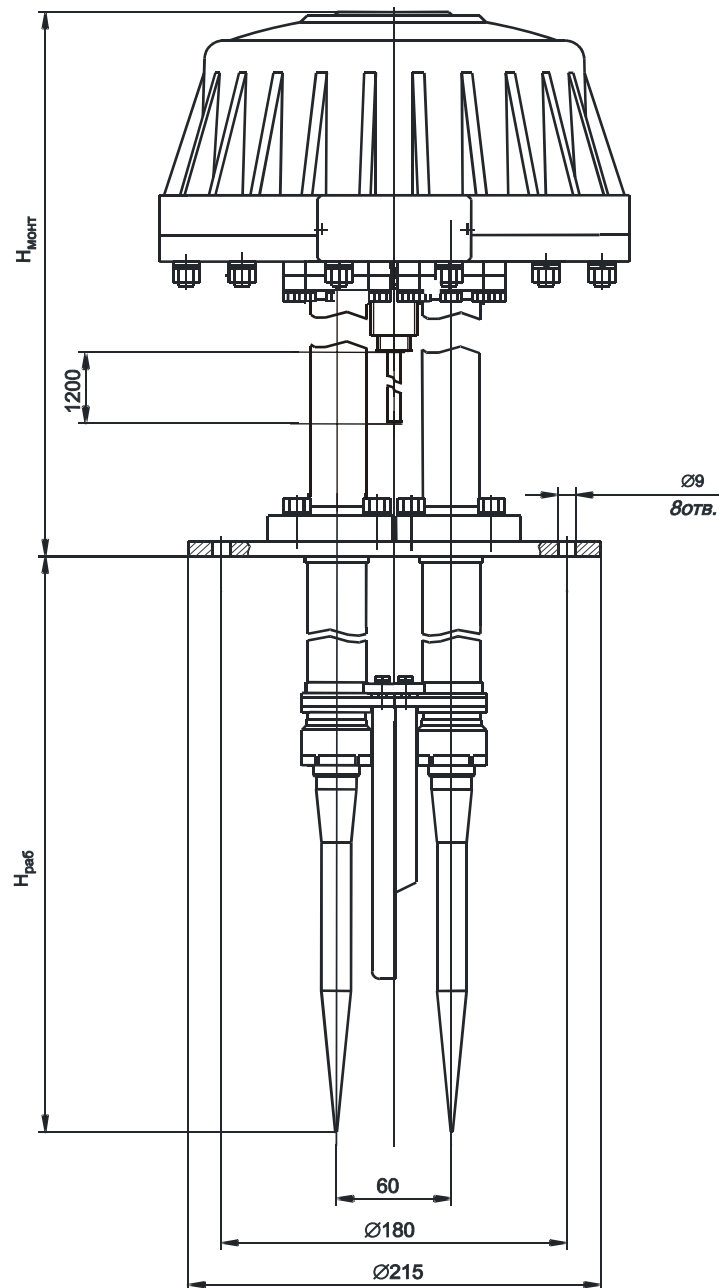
Габаритные и установочные размеры прибора БАРС 352И.18
